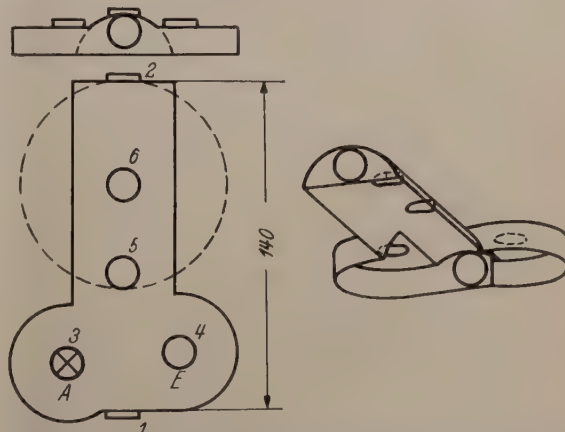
Zylinderkopf langgestreckter Form für den benutzten FN-Motor. 1–6 Bohrungen mit Zündkerzengewinde  $14 \times 1,25$  mm;  $E$  Erhebungsraum für das Einlaßventil;  $A$  Erhebungsraum für das Auslaßventil. Zündkerze in der Bohrung 3.
